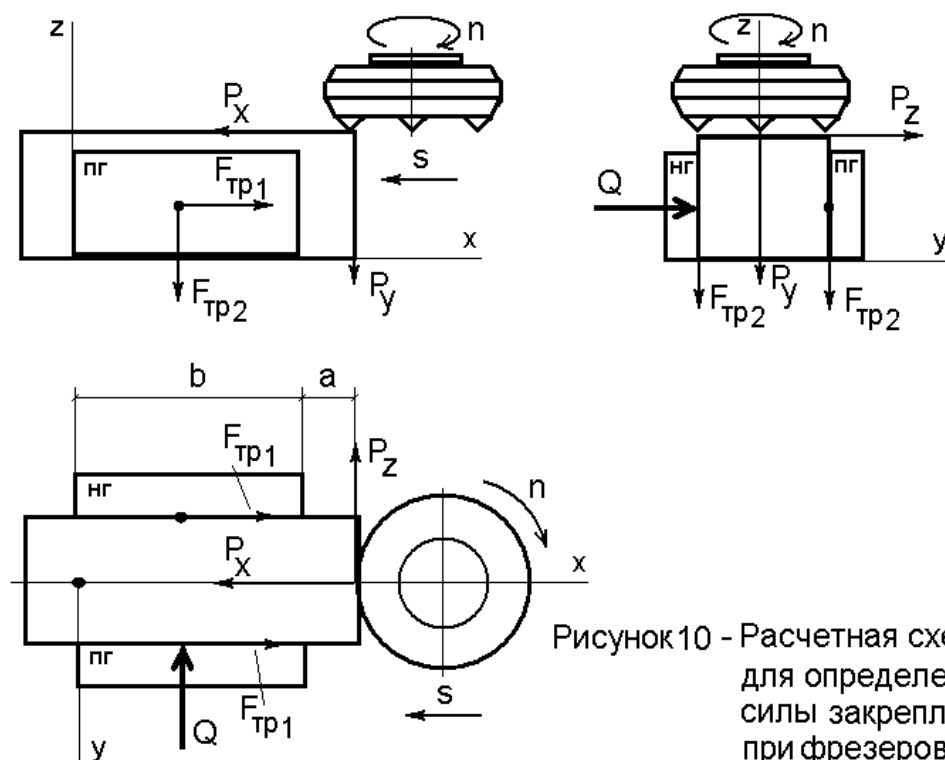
Расчетная схема для определения силы закрепления при фрезеровании
